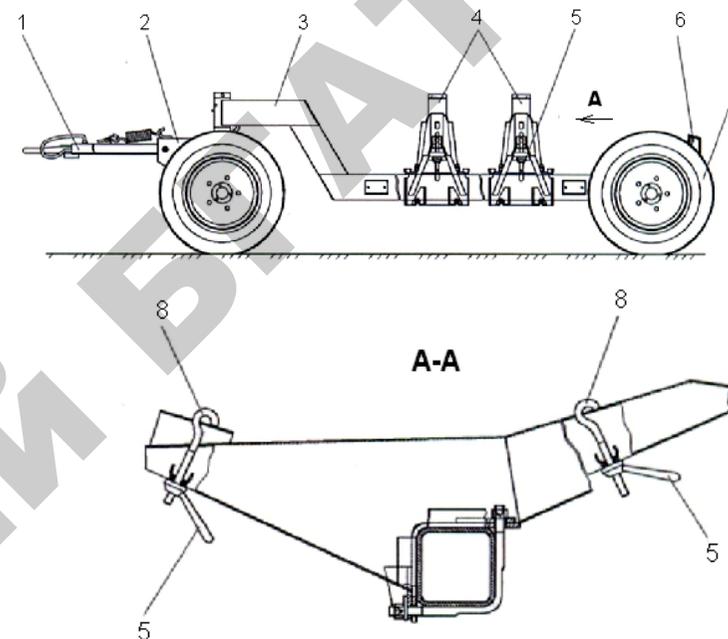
Тележка транспортная: 1 — дышло; 2 — ось передняя; 3 — рама тележки; 4 — ориентир; 5 — зажим; 6 — балка габаритная; 7 — колесо; 8 — зацеп
